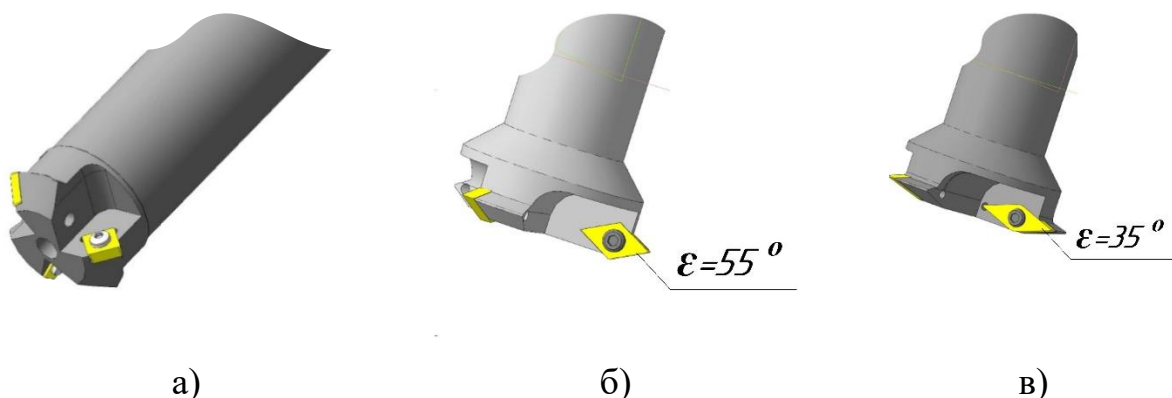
Конструкції непрофільних різальних інструментів для обробки внутрішніх різей: а) – круглої R32; б) – метричної M48x3; в) – дюймової G1½"
